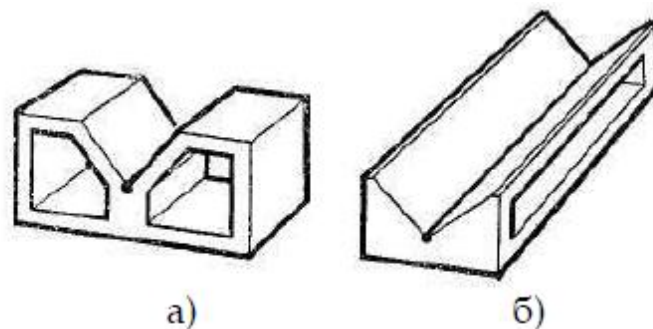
38. Призми: а – для заготовок великих діаметрів; б – для заготовок малих діаметрів
